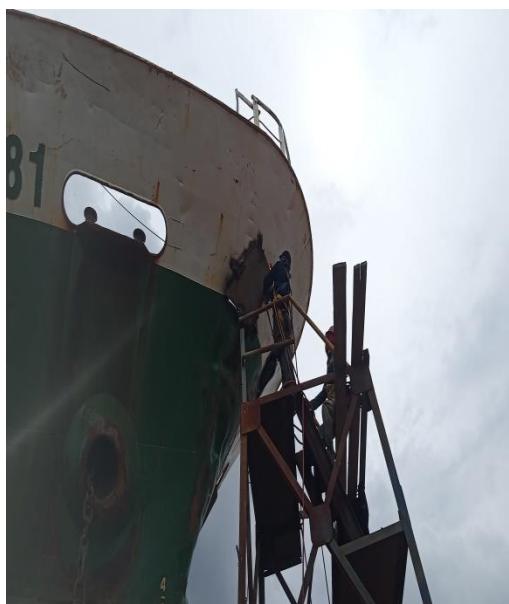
Repair Lidah-lidah Ramp door depan kapal KMP Gurare.
